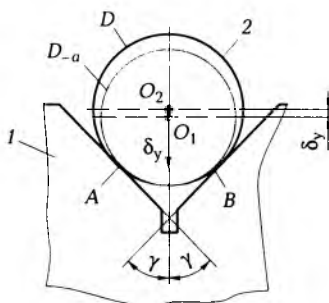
Схема установки базы «вал» на установочную призму:
